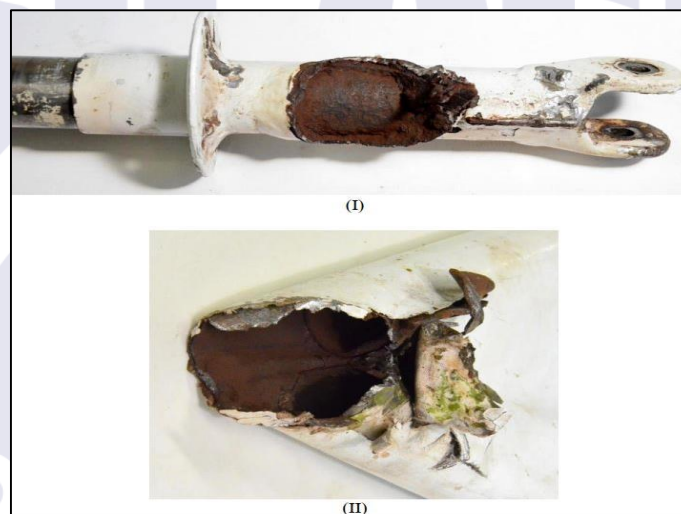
Eixo da roda com fratura no cordão da solda e corrosão generalizada (I) e perna do trem de pouso com fratura e corrosão generalizada (II).
